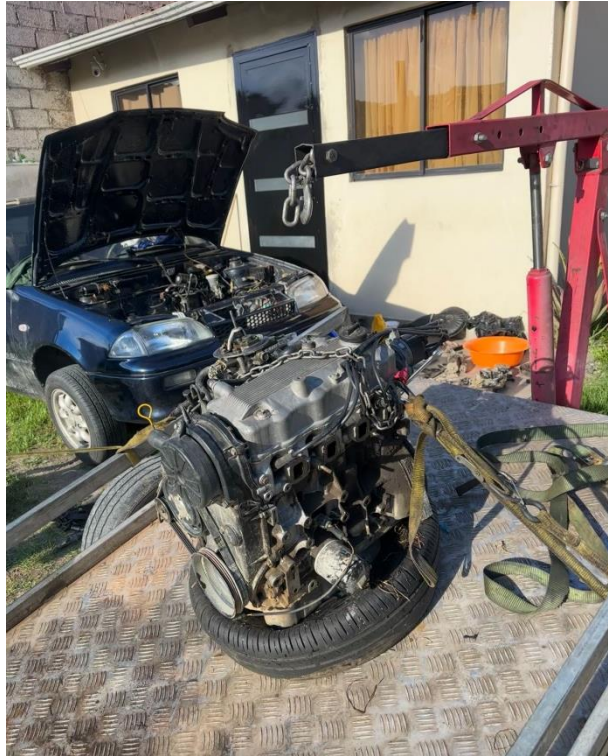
DESMONTAJE DE CAJA DE CAMBIOS Y KIT DE EMBRAGUE
